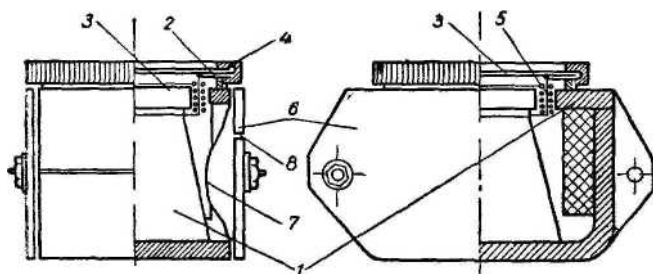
Подводный громкоговоритель: 1 — магниты, 2 — дюралюминиевое кольцо; 3 — мембрана; 4 — зажимное кольцо; 5 — звуковая катушка, 6 — крышки, 7 — резиновая пленка, 8 — отверстия в крышке,
